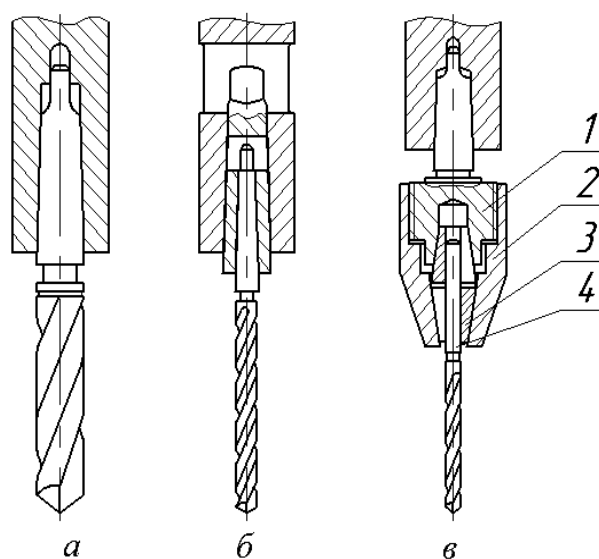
Схеми закріплення інструментів у шпинделях свердлильних верстатів
